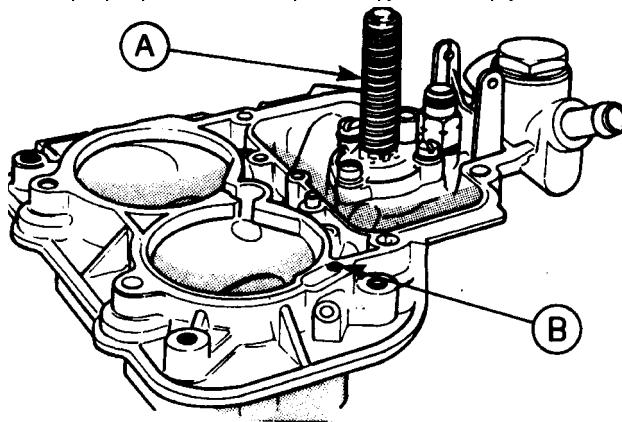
Детали устройства облегчения пуска холодного двигателя - карбюратор WEBER. А - Мембра. В - Пружина. С - Корпус.
